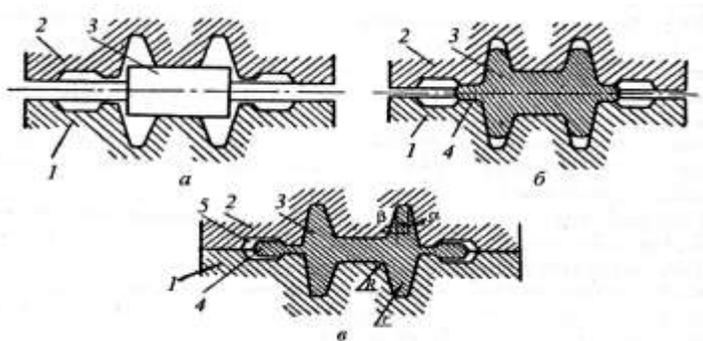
Штамповка в открытом штампе: а – начальная стадия; б – стадия образования заусенца; в – конечная стадия штамповки; 1, 2 – нижняя и верхняя половины штампа; 3 – исходная заготовка; 4 – заусенец; 5 – заусеничная канавка
